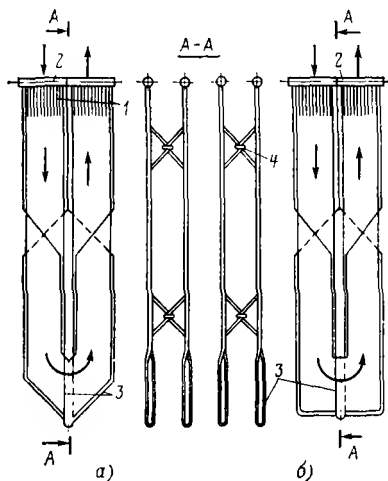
Вертикальный ширмовый пароперегреватель:
